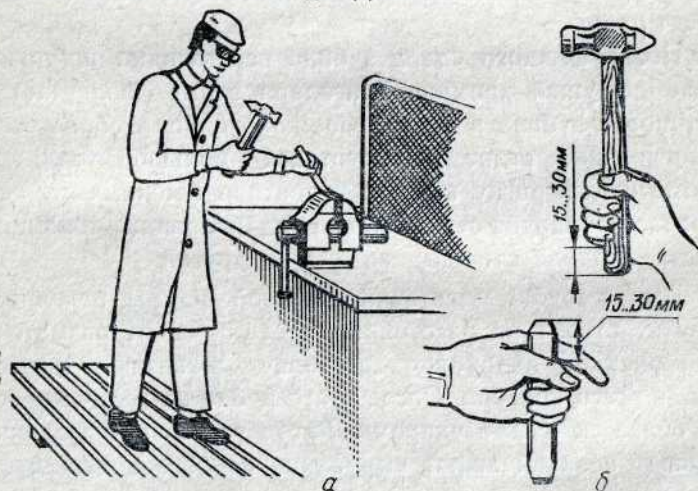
Рубка: а — рабочая поза; б — хватка инструмента.
